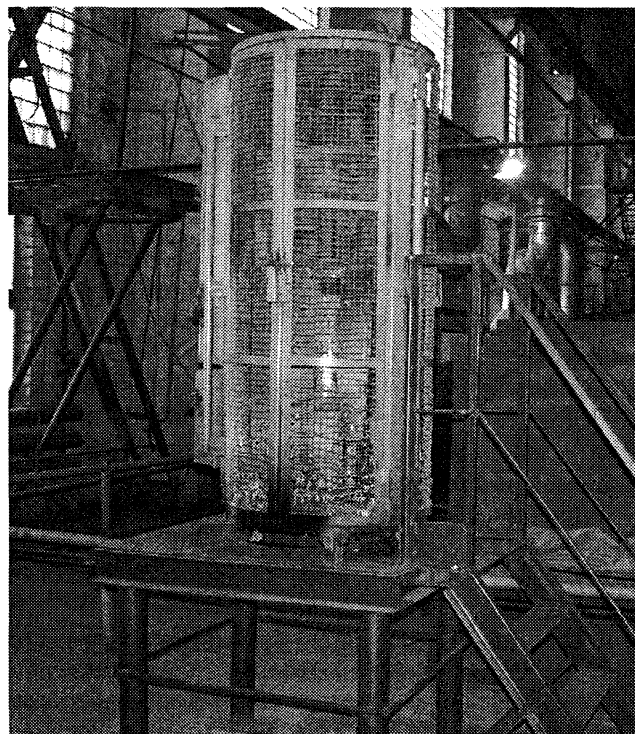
Установка мод. 46161 для металлургической обработки алюминиевого расплава
